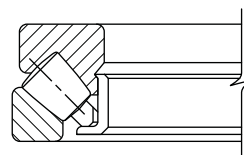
Axial-Pendelrollenlager des Typs TSR
